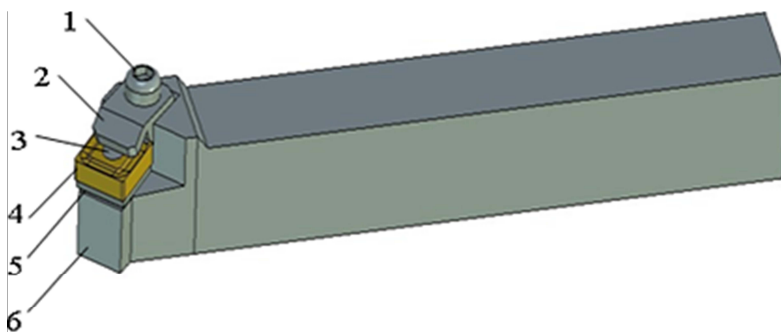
Резец проходной наружный с креплением СМП клин-прихватом (тип *M*):
